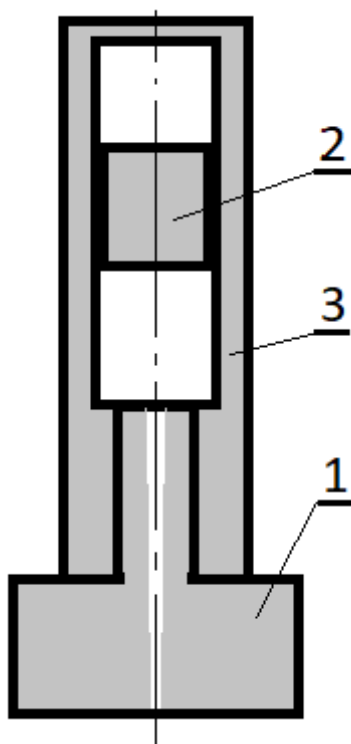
Звичайний занурний пневмоударник: 1- буровий інструмент; 2 – поршень-ударник; 3 – корпус
